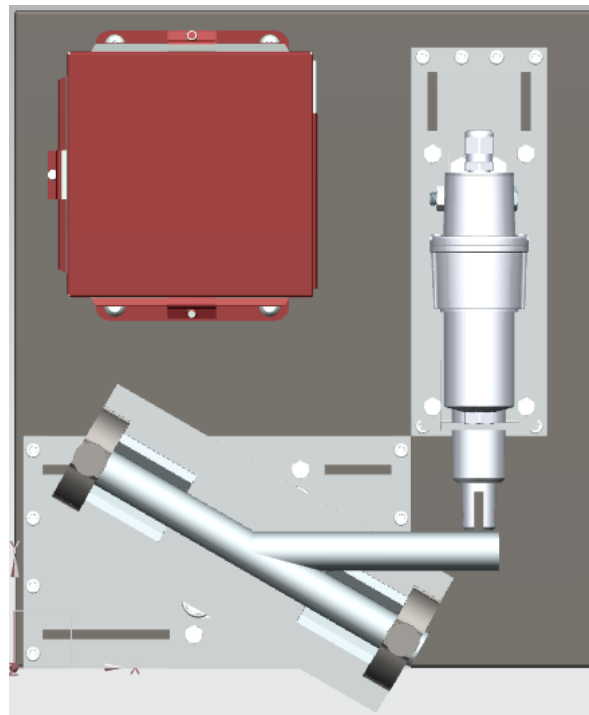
Vista superior de máquina con probeta a 30° montada.
